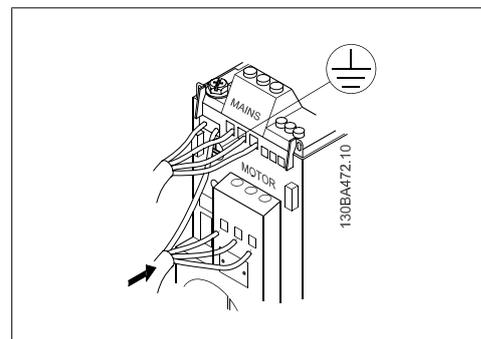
Befestigung von Erd- und Motorkabeln.
